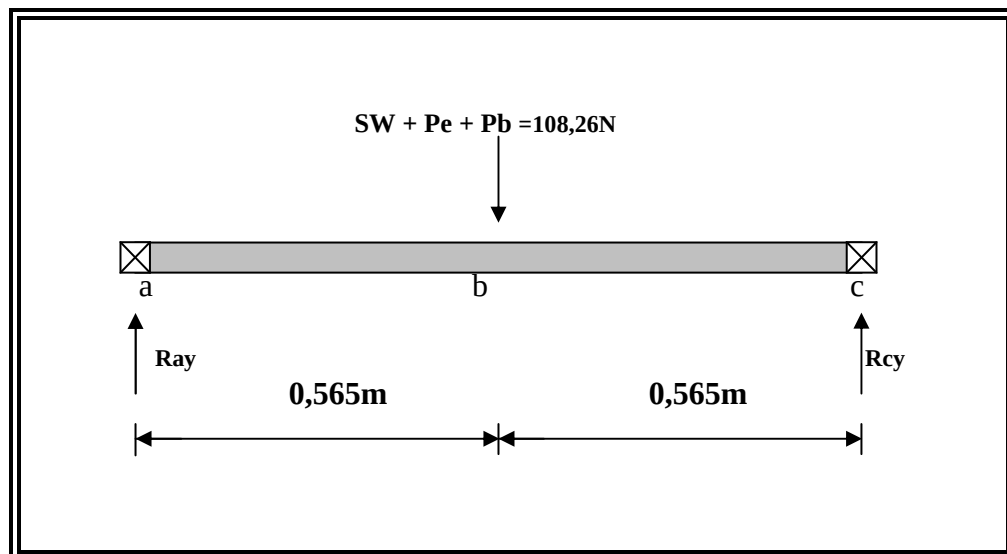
Fuerzas aplicadas sobre el eje en el plano “XZ” del transportador N° 3. Fuente: Elaboración propia.
